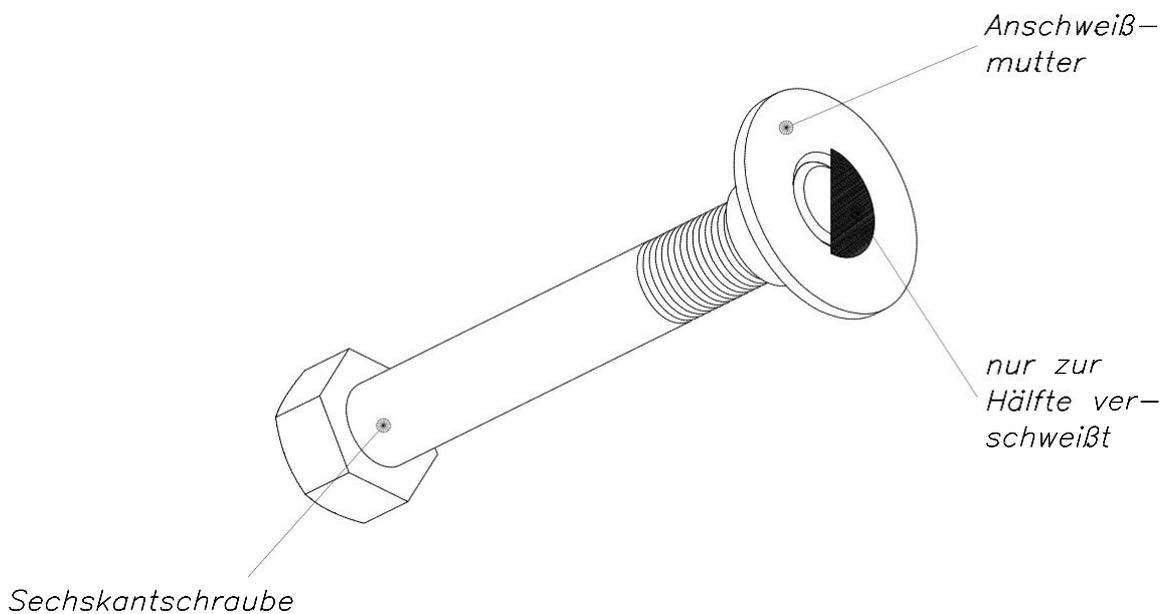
Beispiel einer inneren Verschweißung
